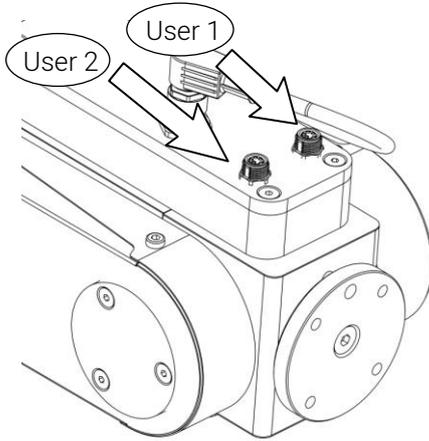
elektrische Anschlüsse für Werkzeuge
